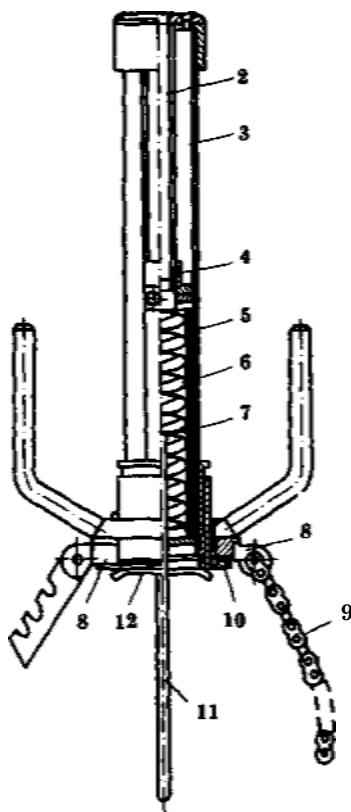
Прибор для намерения глубины загнивания древесины с помощью иглы: 1 — ручки; 2 — винт; 3 — корпус; 4, 10 — гайки; 5 — внутренний цилиндр; 6 — пружина; 7 — указатель; 8 — ушки; 9 — цепь; 11 — игла; 12 — упор
